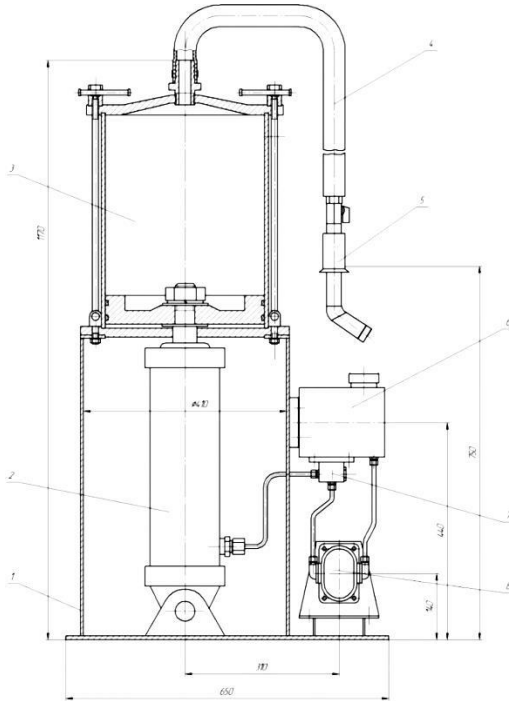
Универсальный стенд для откачки и подачи масла: 1-рама; 2-гидроцилиндр; 3- рабочий цилиндр стенда; 4- рукав подачи или отсоса масла; 5-пистолет (головка для установки в горловину); 6-бак для масла; 7-гидрораспределитель; 8-насос высокого давления.
